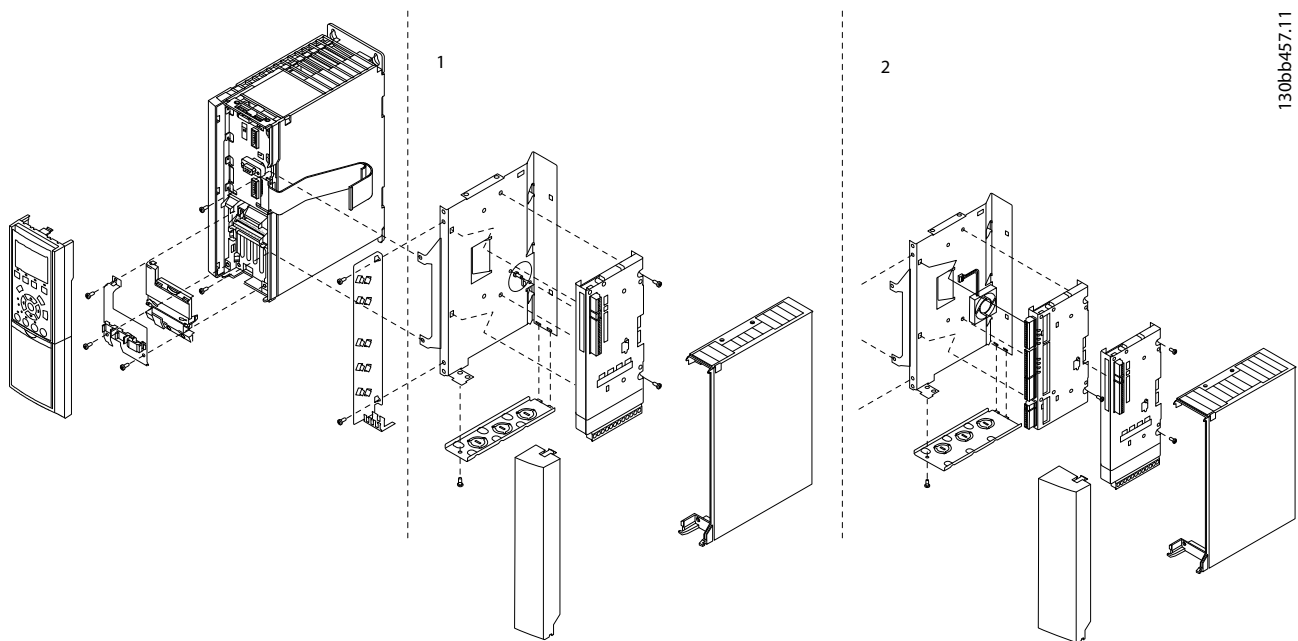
Installation der VLT® Extended Relay Card MCB 113 – Explosionszeichnung
